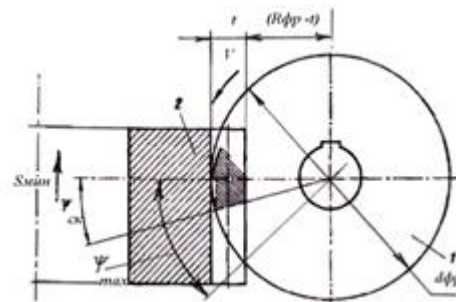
Схема расчета параметров обработки при зубофрезеровании зубчатых колес
